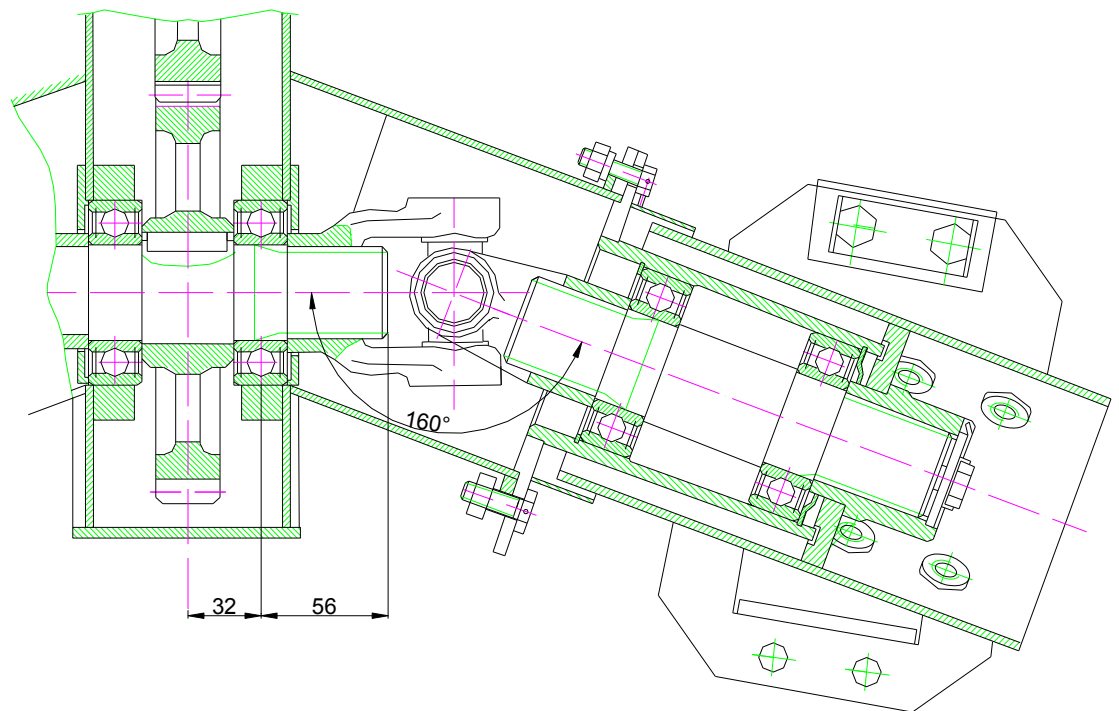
Фрагмент креслення базової конструкції тихохідного вала редуктора
